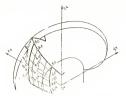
Сеть координатных линий на боковой затылованной поверхности червячной фрезы
